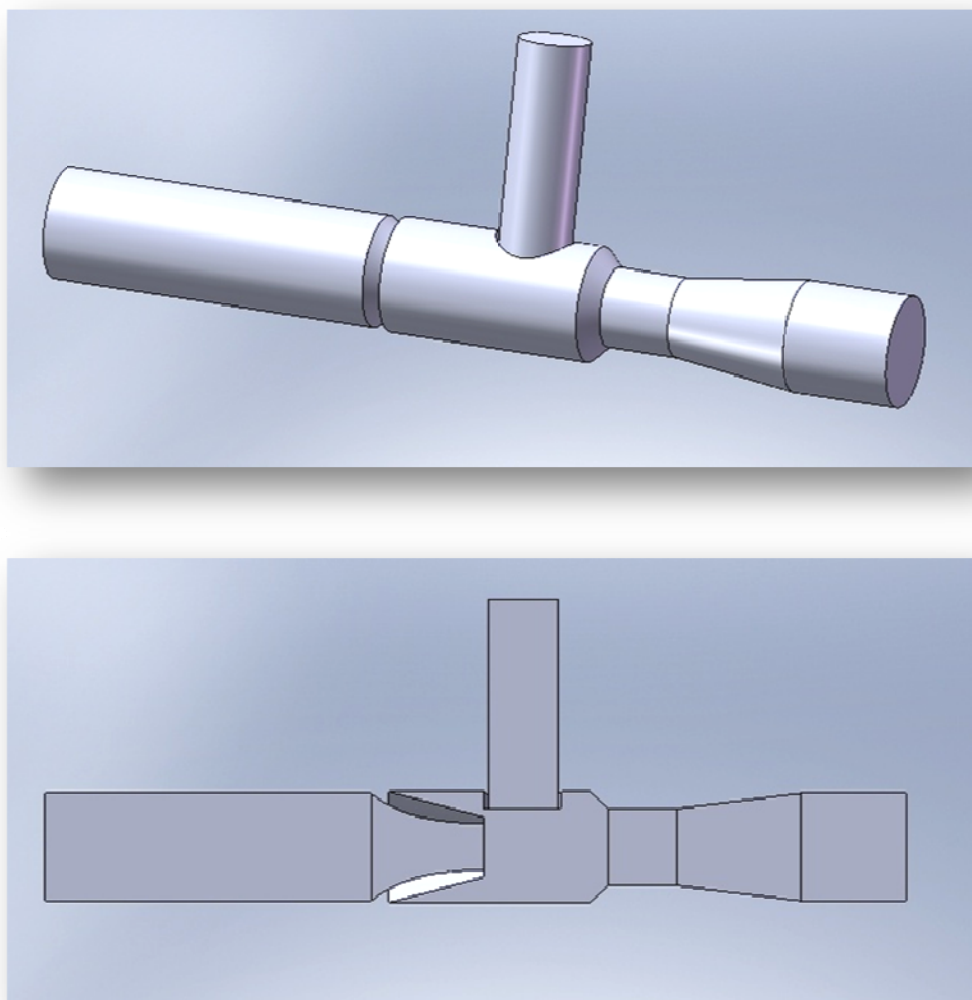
Upravená geometrie ejektoru pro modelování proudění v CFD
